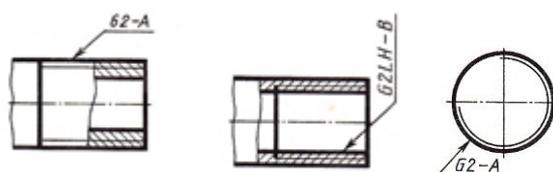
Обозначение резьбы трубной цилиндрической
